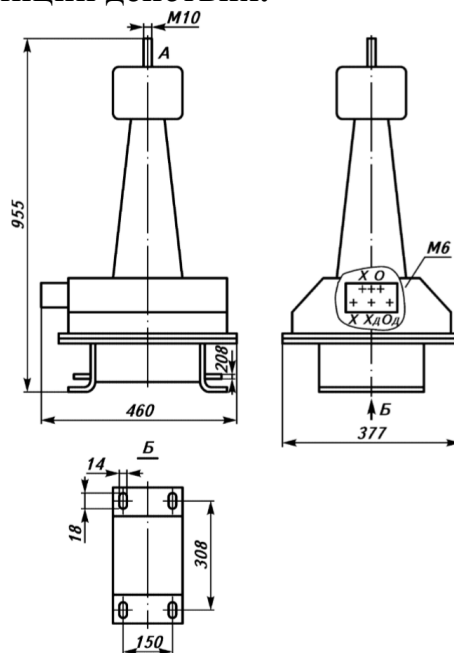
Общий вид, габаритные и установочные размеры трансформатора
